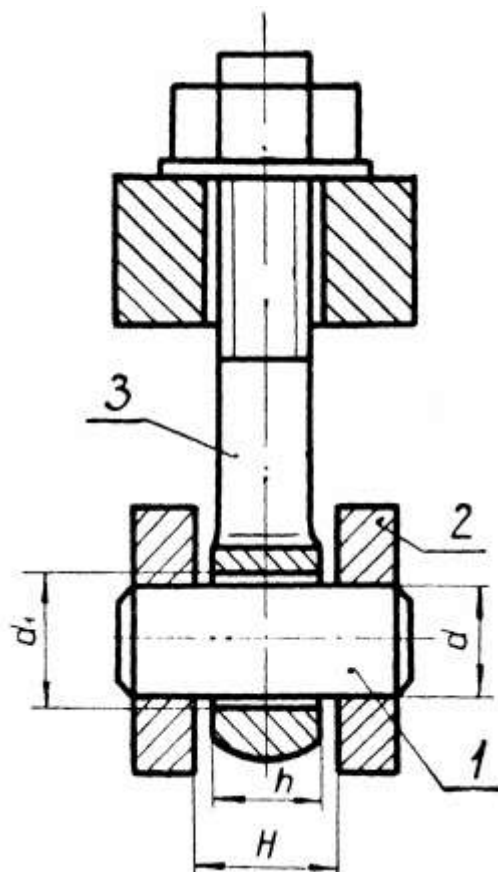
Неподвижное соединение пальца поз. 1 с корпусом поз. 2
